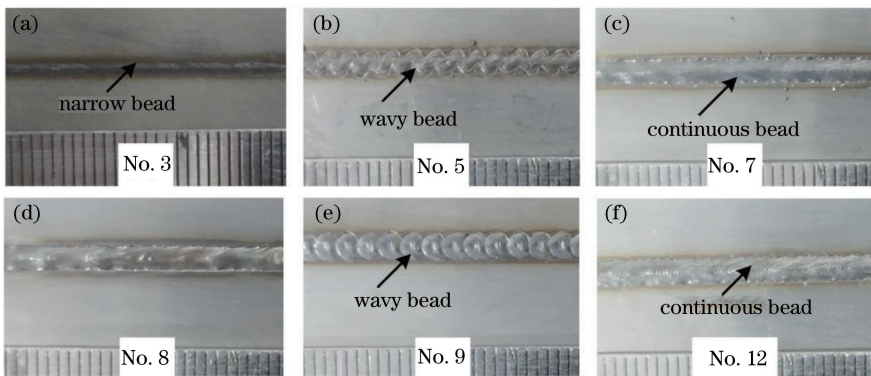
典型焊接参数下获得的焊缝的宏观形貌
